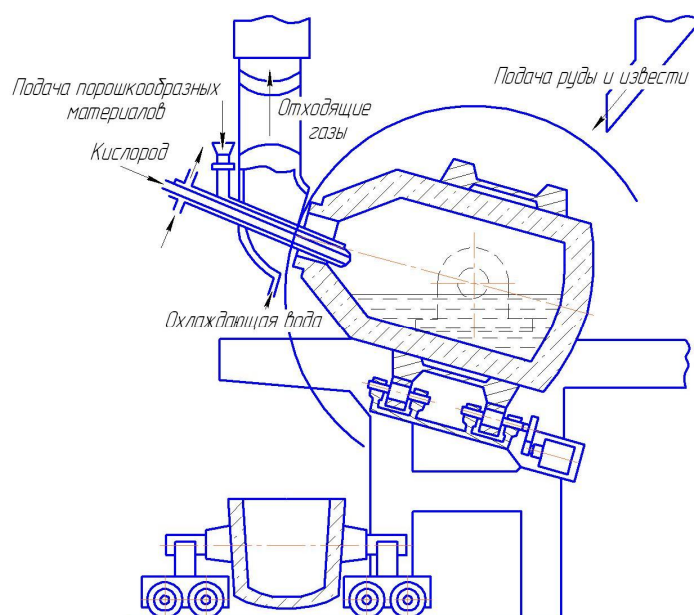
Схема конструкции конвертера для реализации Калдо-процесса
